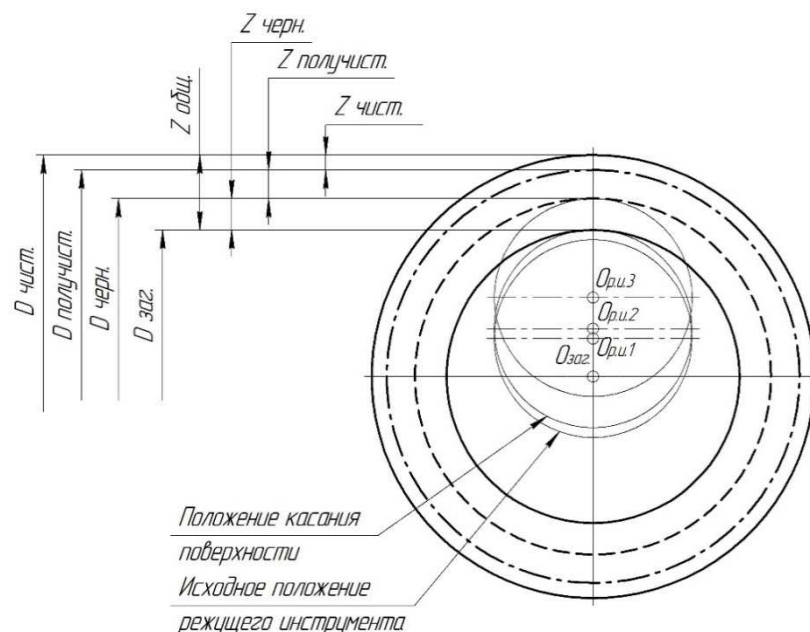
Схема съема общего припуска черновым, полуристовым и калибрующим зубом гребенчатой фрезы с зачищающей режущей кромкой
